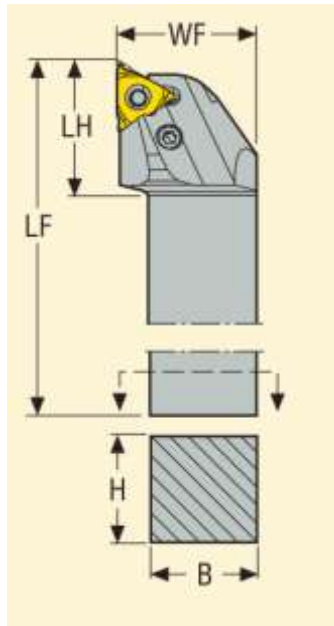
Державка резца для нарезания резьбы на валу К-12-11
